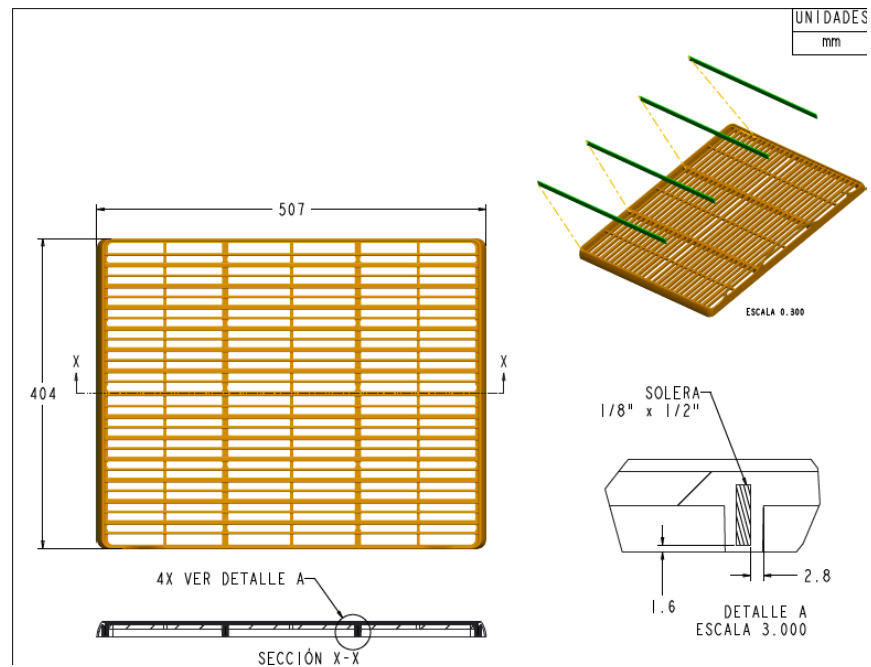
Parrilla híbrida “plástica-metálica” refuerzos paralelos
